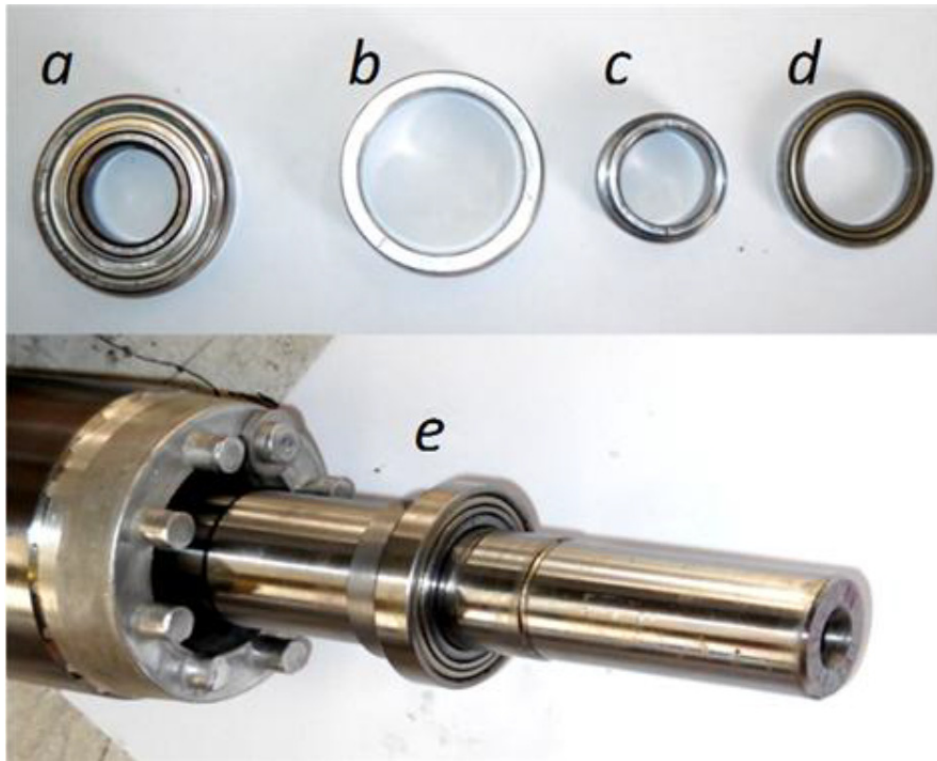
2 Superior: Rodamiento fabricado con defecto (a) y su despiece en casquillo externo (b), casquillo interno (c) y parte central (d). Inferior: Montaje del rodamiento defectuoso en el eje del rotor del motor.
